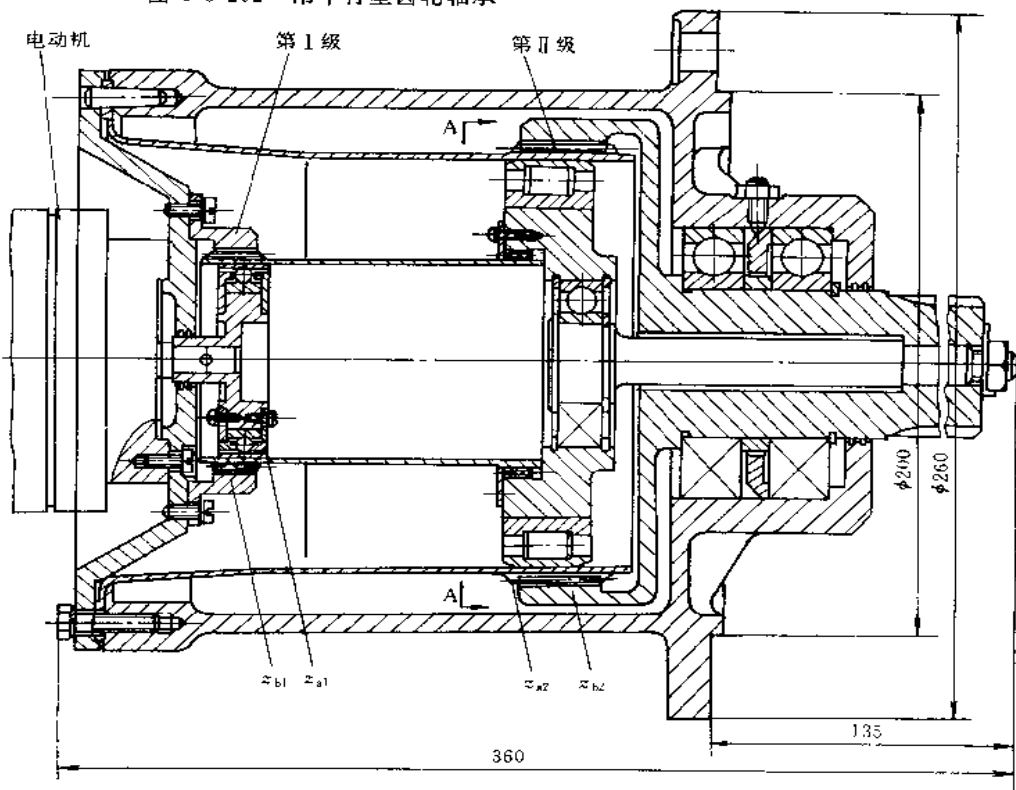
所示吊车行星齿轮系统负荷大,空间小,若采用标准轴承,齿轮必须有一薄壁部分,导致齿轮疲劳寿命的降低,如选用 FAG 公司产品以齿轮一部分为外圈(如图 1-5-292 的 I 放大)的 E 鼓形调心滚子轴承,就可满足使用要求。
